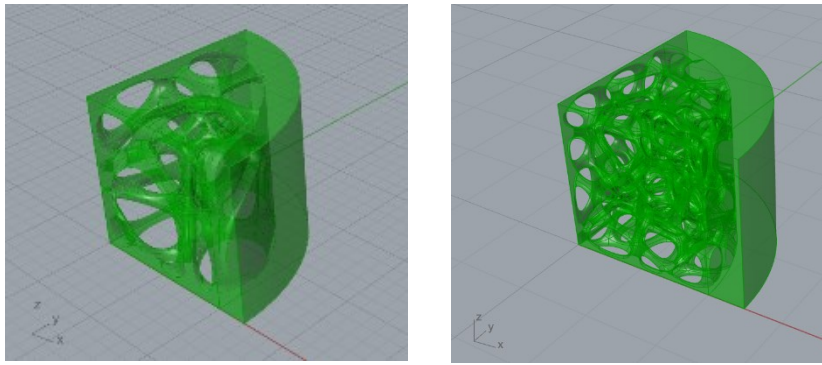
Osso Intero A) dimensioni iniziali di 10mm B) dimensioni iniziali di 2mm.
